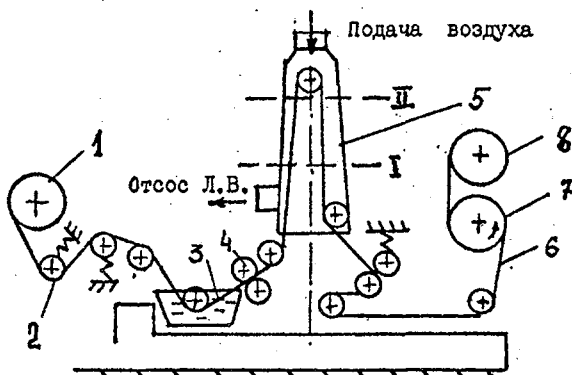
Схема пропиточной установки УПСТ: 1 — катушка с лентой; 2 — устройство натяжное; 3 — ванна пропиточная; 4 — устройство отжимное; 5 — камера сушильная; 6 — препрег; 7 — механизм намотки; 8 — катушка с полиэтиленовой пленкой
